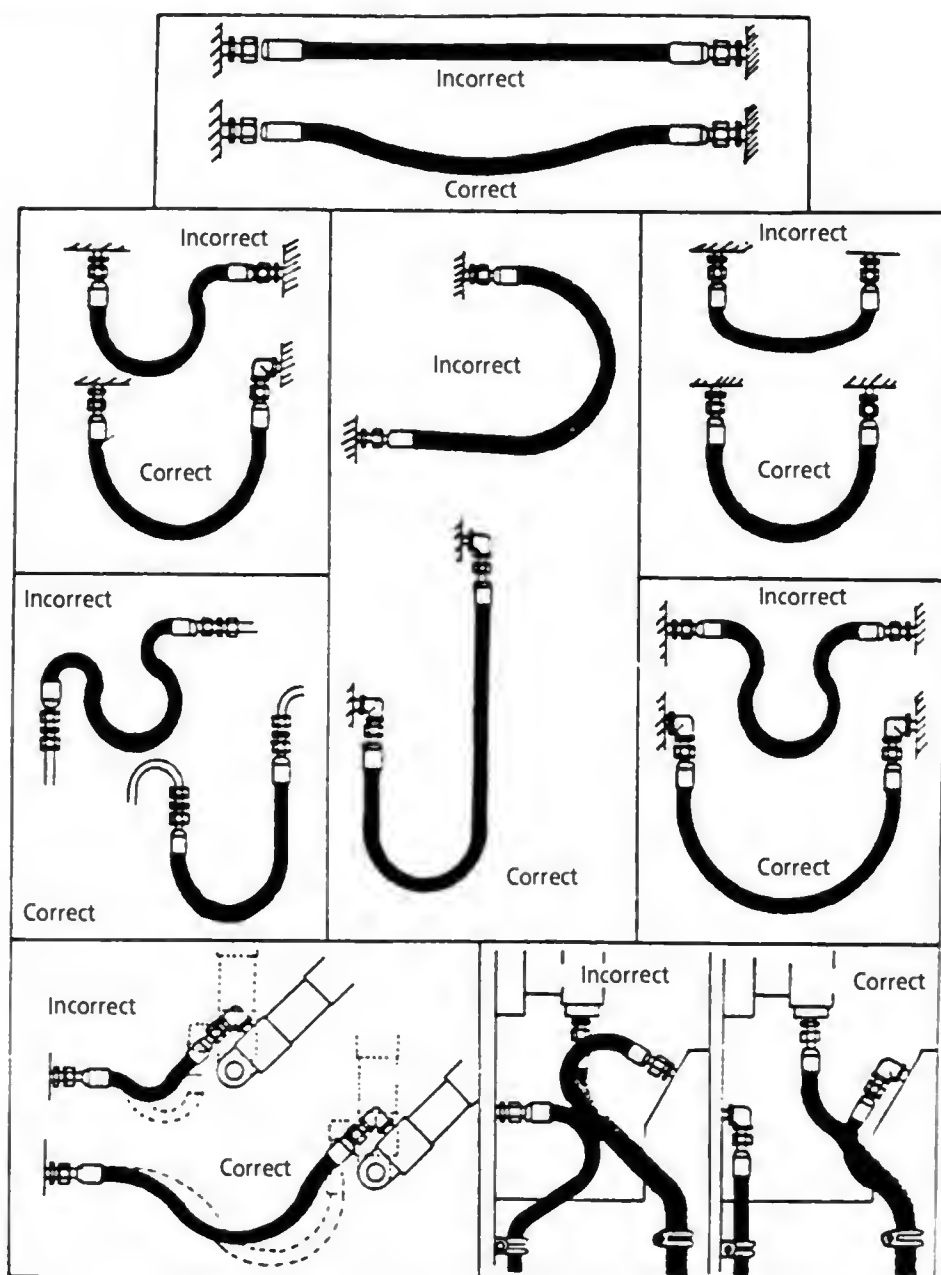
Règles de montage des flexibles hydrauliques.
